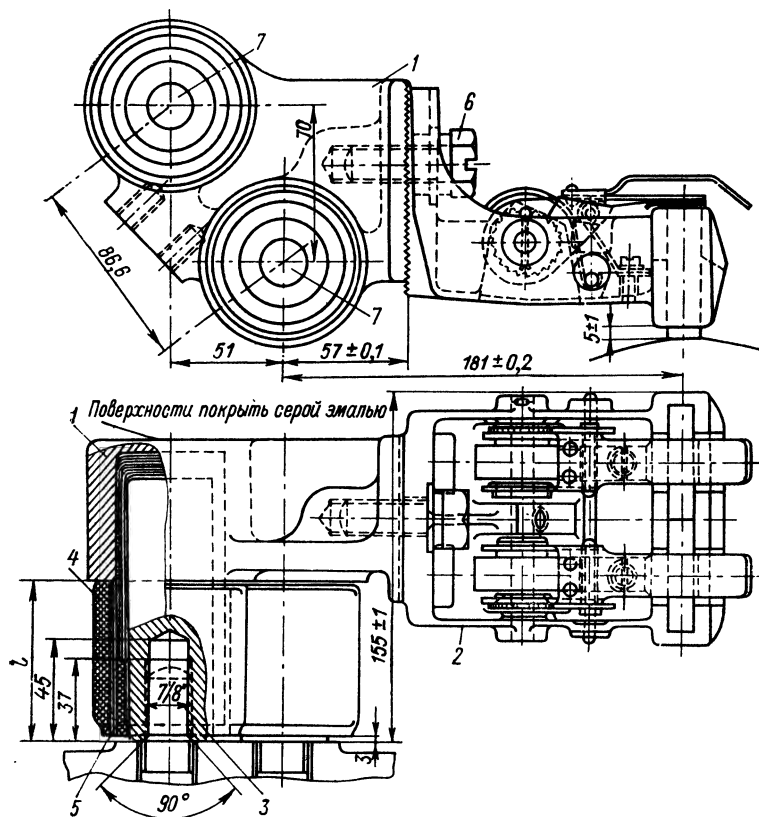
Щеткодержатель электровозного тягового двигателя
